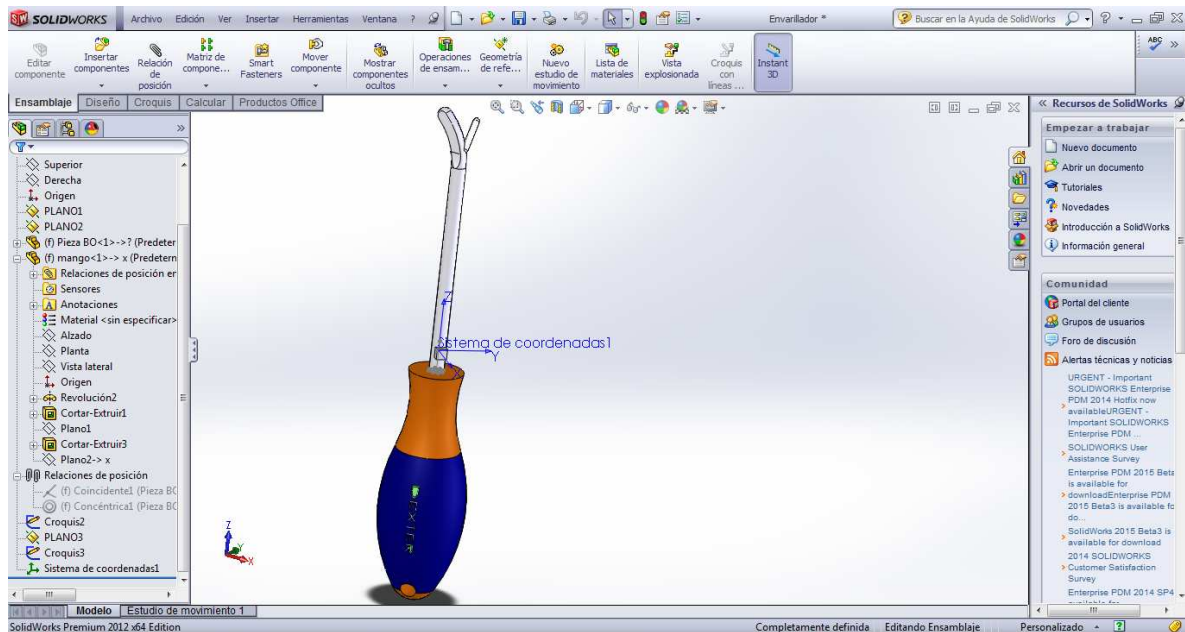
Vista 1 del conjunto completo (herramienta+acelerómetro) en SOLIDWORKS
